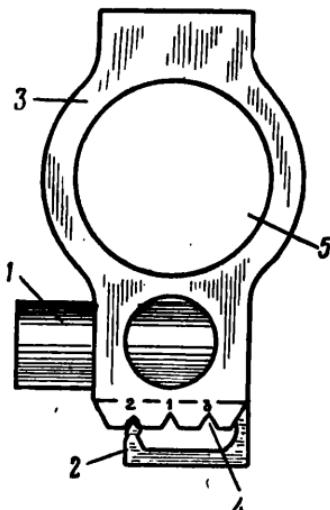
Регулятор установлен с левой стороны ротного пулемета (по ходу стрельбы). Зуб фиксатора можно совмещать со второй или третьей канавкой газовой каморы (обозначены цифрами 1 и 2):
